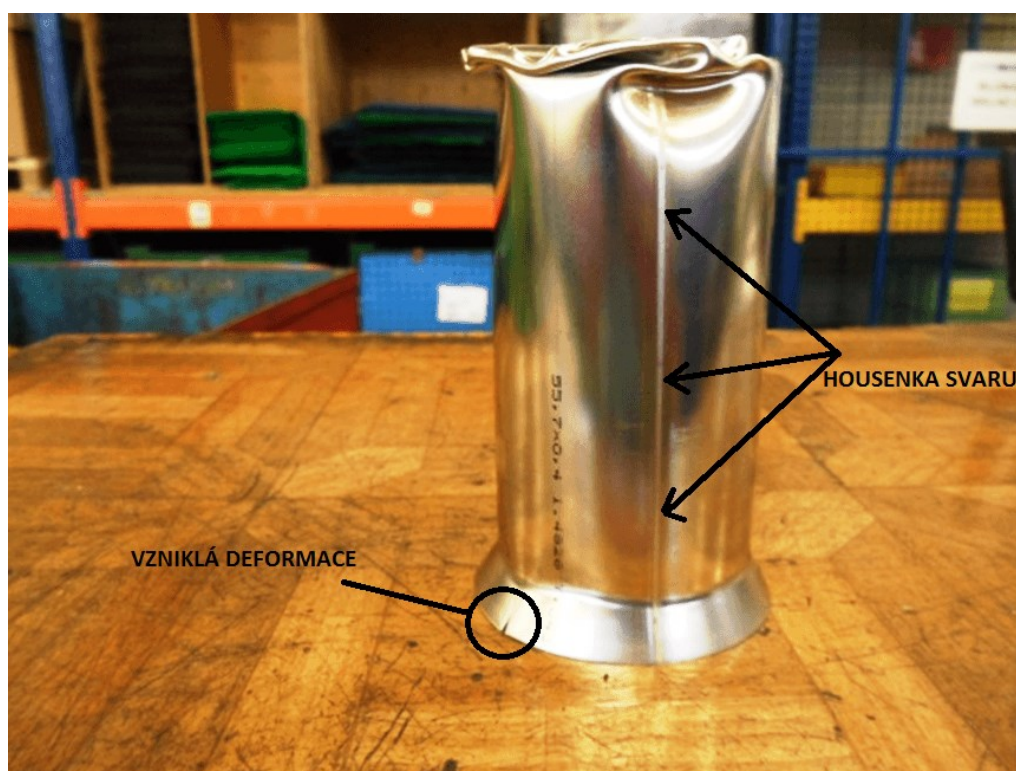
Ukázka deformace na vzorku způsobena vyboulením [15]
